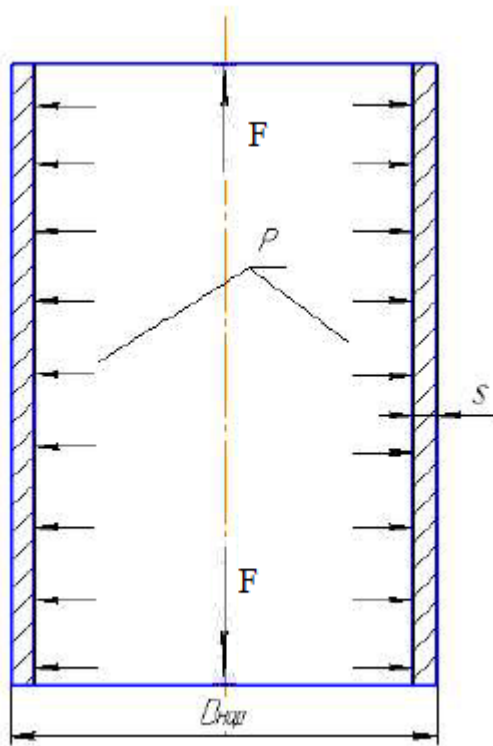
Расчетная схема цилиндрической обечайки колпака
